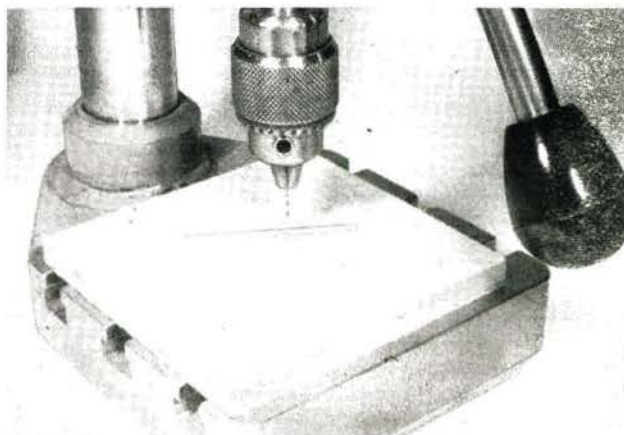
Viereckige Blechplättchen werden viermal jeweils mit einer Ecke gegen einen Winkelanschlag gedrückt und mit eingespanntem Körner maschinell angekört.
